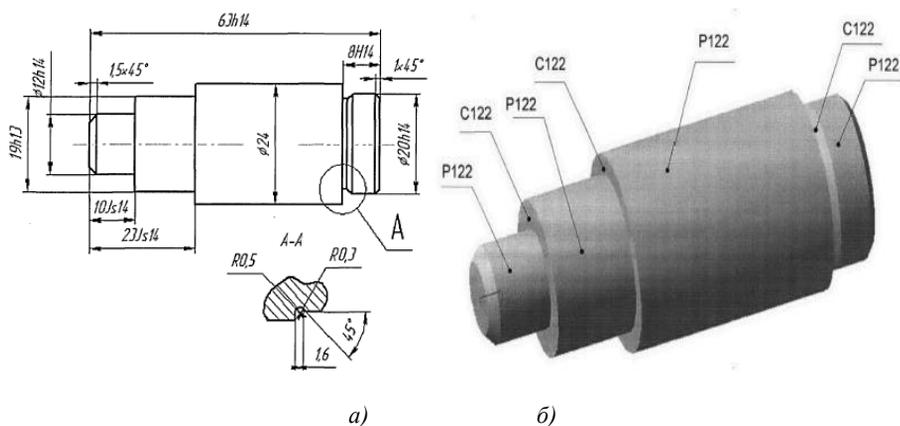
а) пример детали типа «вала»; б) конструктивные элементы вала
